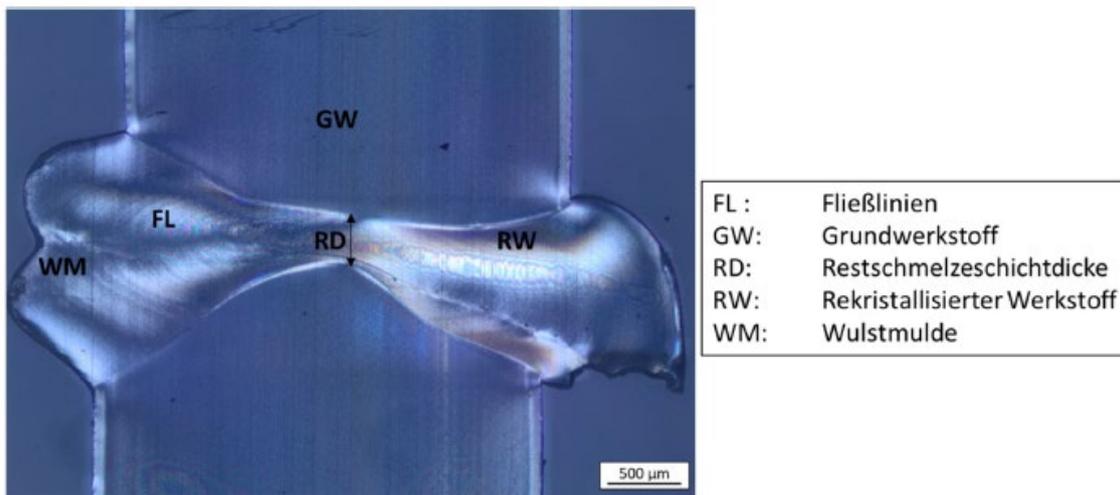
Durchlichtaufnahme (90°-Polarisation) einer Laserstumpfstoßschweißnaht mit PE-HD
